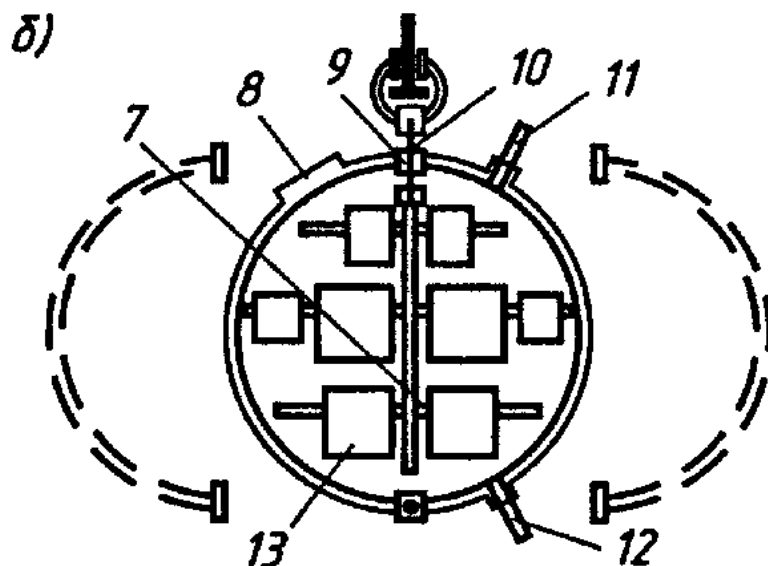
(б). Полуавтоматическая установка АВБ-4 для пропитки под вакуумом и давлением схема автоклава и подвески: 7 – подвеска; 8 – смотровое окно; 9 – уплотнения; 10 – металлическая пластина; 11, 12 – штуцера; 13 – предназначенный для пропитки статор (ротор)
